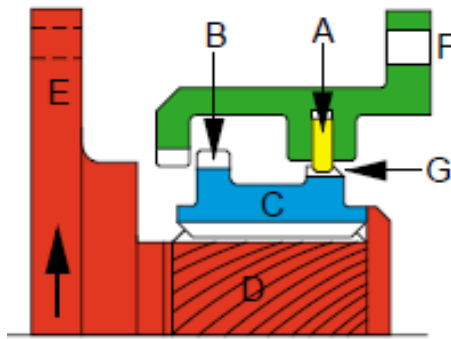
Embrague enganchado al trinquete. Componente deslizante detenido [37].
